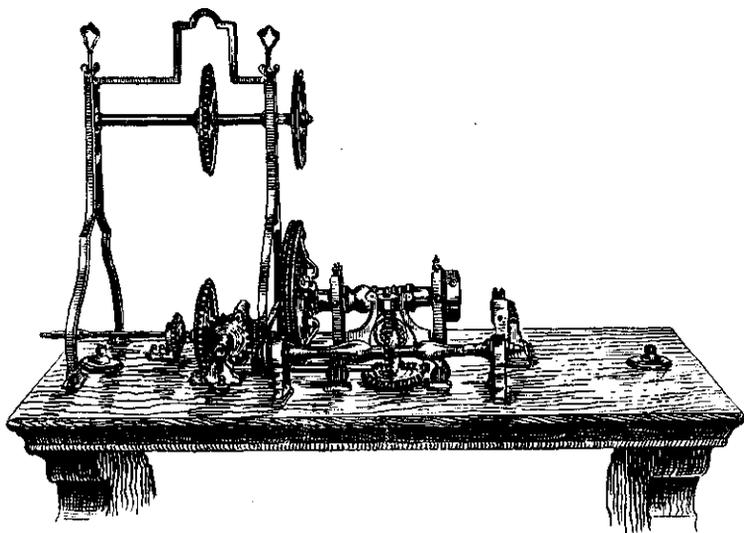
Токарно-копировальный медальерный станок Яковлева -- Нартова (общий вид).
